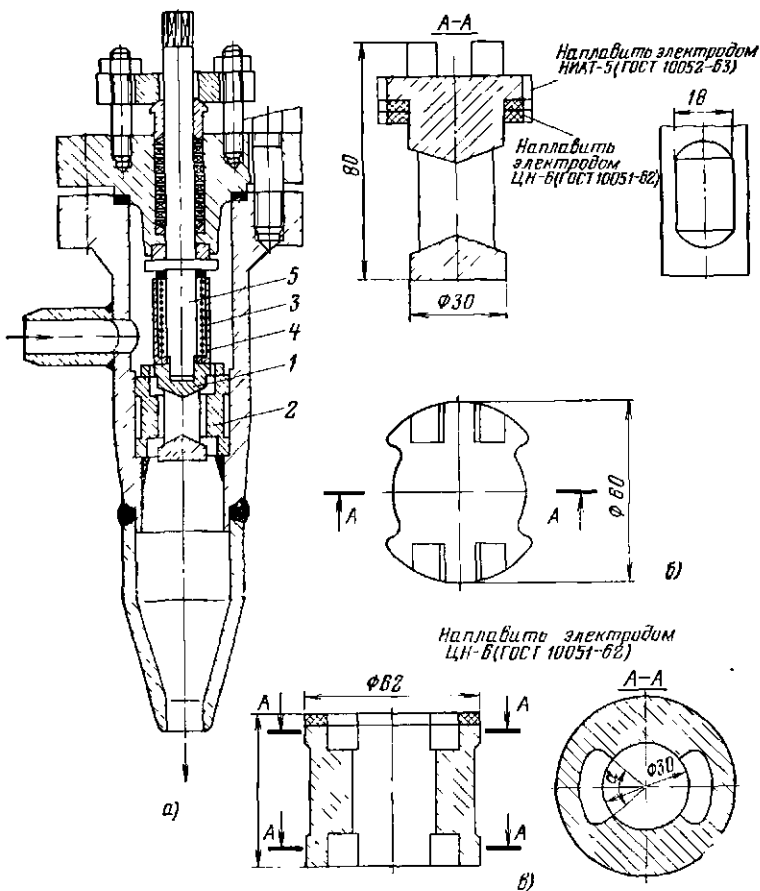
Многоступенчатый регулирующий клапан  $D_v$  20 мм поворотной конструкции.
